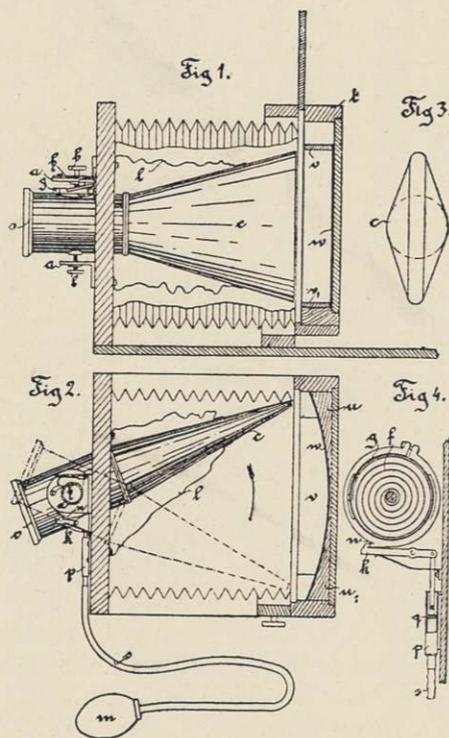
Vue de la chambre dans le sens vertical. — Fig. 2. Vue de la chambre dans le sens horizontal.
